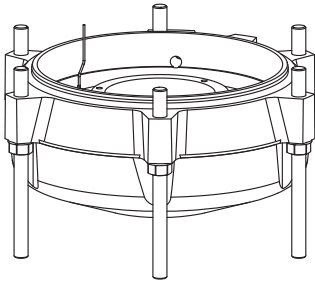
Montage de la plaque d'usure (J 205, J 405)
